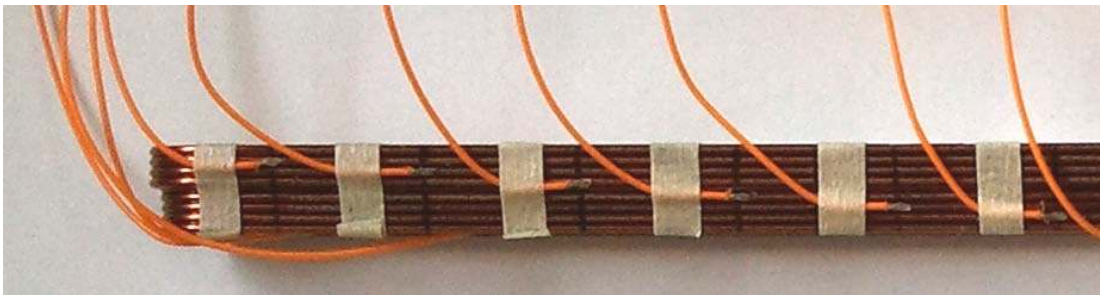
Aperçu d'une partie de la bobine avec les points de soudure.
